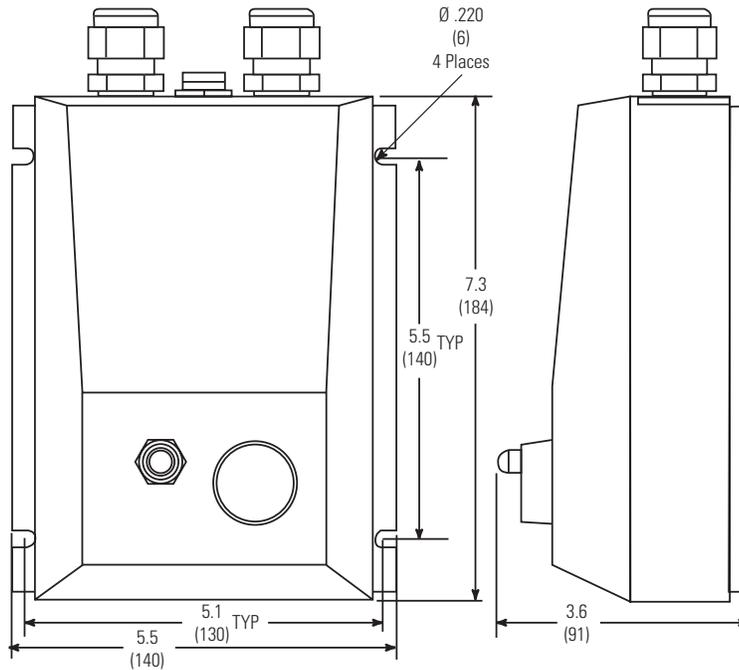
Dimensions de montage de boîtier de commande 77111-10, 77111-15, 77111-40 et 77111-47.
